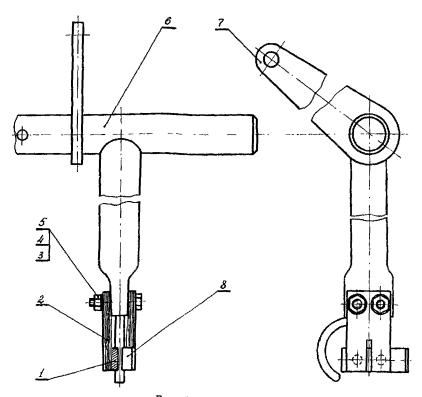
Нож заземления: I - кентакт; 2 - пружина; 3 - гайка МВ; 4 - шайба пр.8Н; 5 - болт МВж35; 6 - вал; 7 - рычаг; 8 - кентакт
